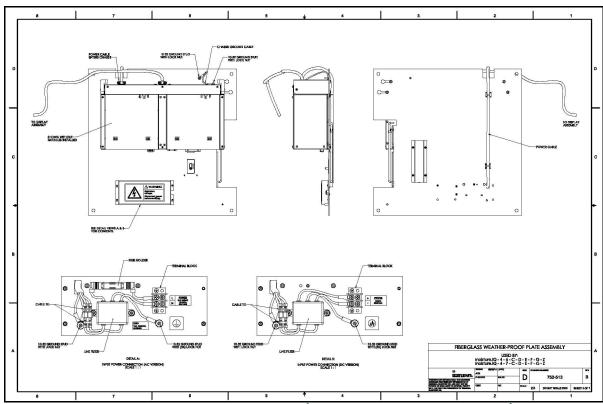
Conjunto de placas WP (desenho 752-513\_revB, SH 3 de 5)
